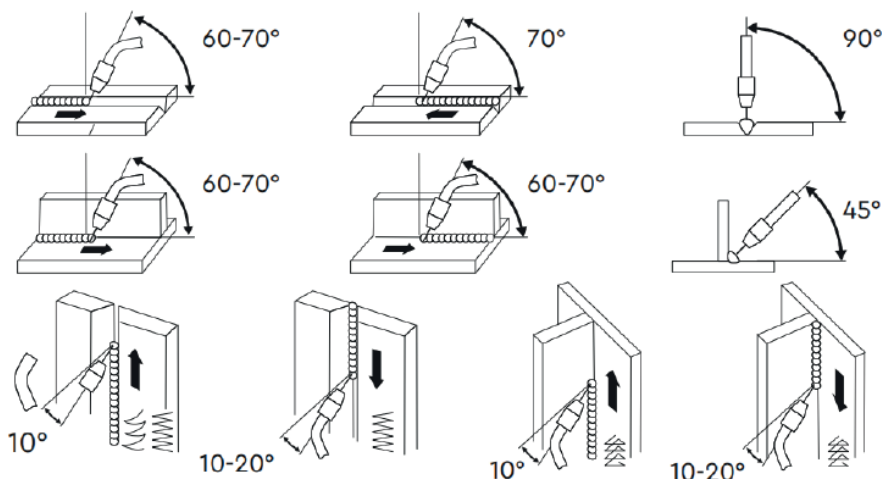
Кут розташування електрода із покриттям до деталі під час ручного дугового зварювання («ММА»).
